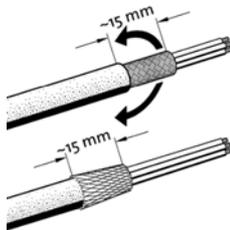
Pålegging av kabelisoleringer på EMC-kabelskjøter med gjenger (SC...FC WM)
